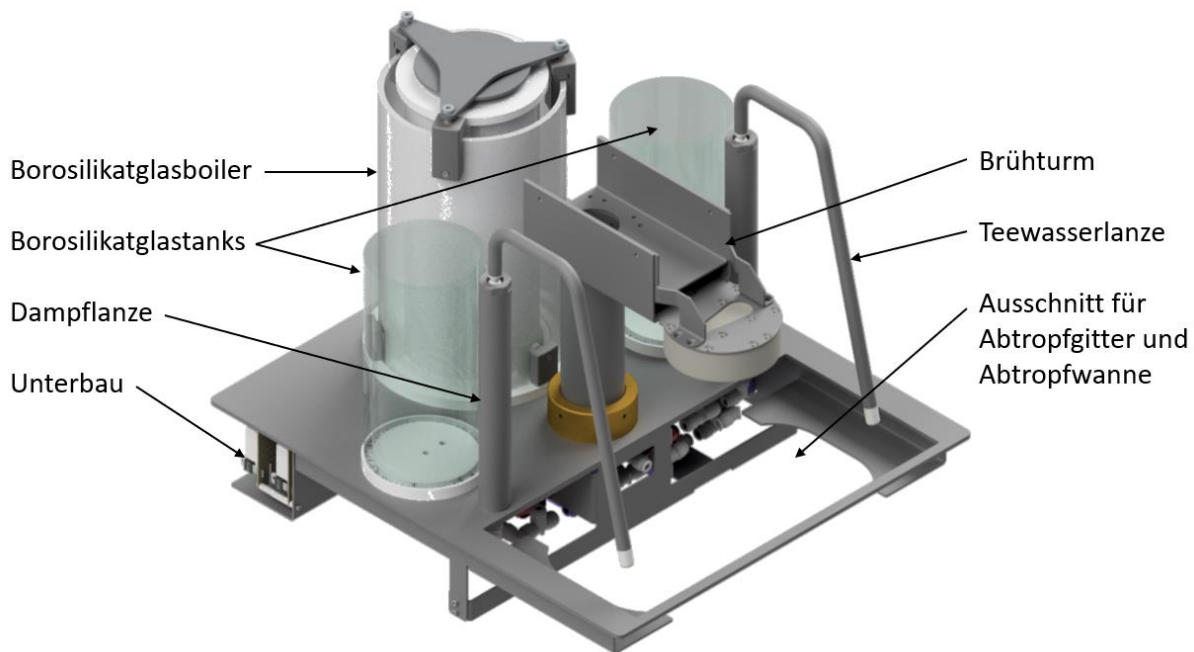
Isometrische Ansicht der Glasboiler Espressomaschine „Style“
